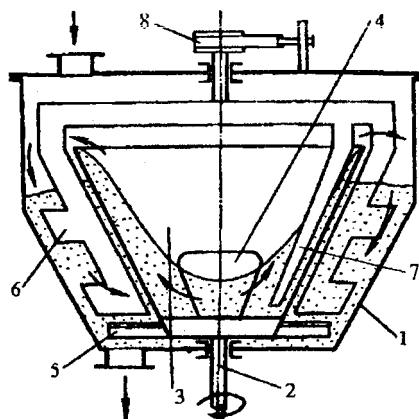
Конусны цэнтрабежны змяшальнік: 1— корпус; 2 — вал;
